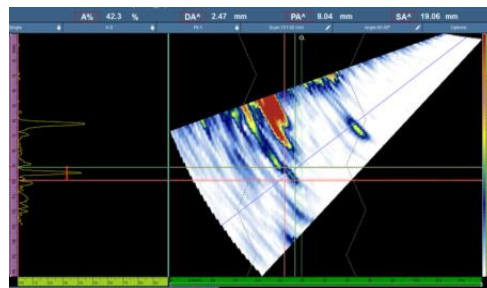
Defeito 3 da região 1 com junta soldada pelo processo MIG.
